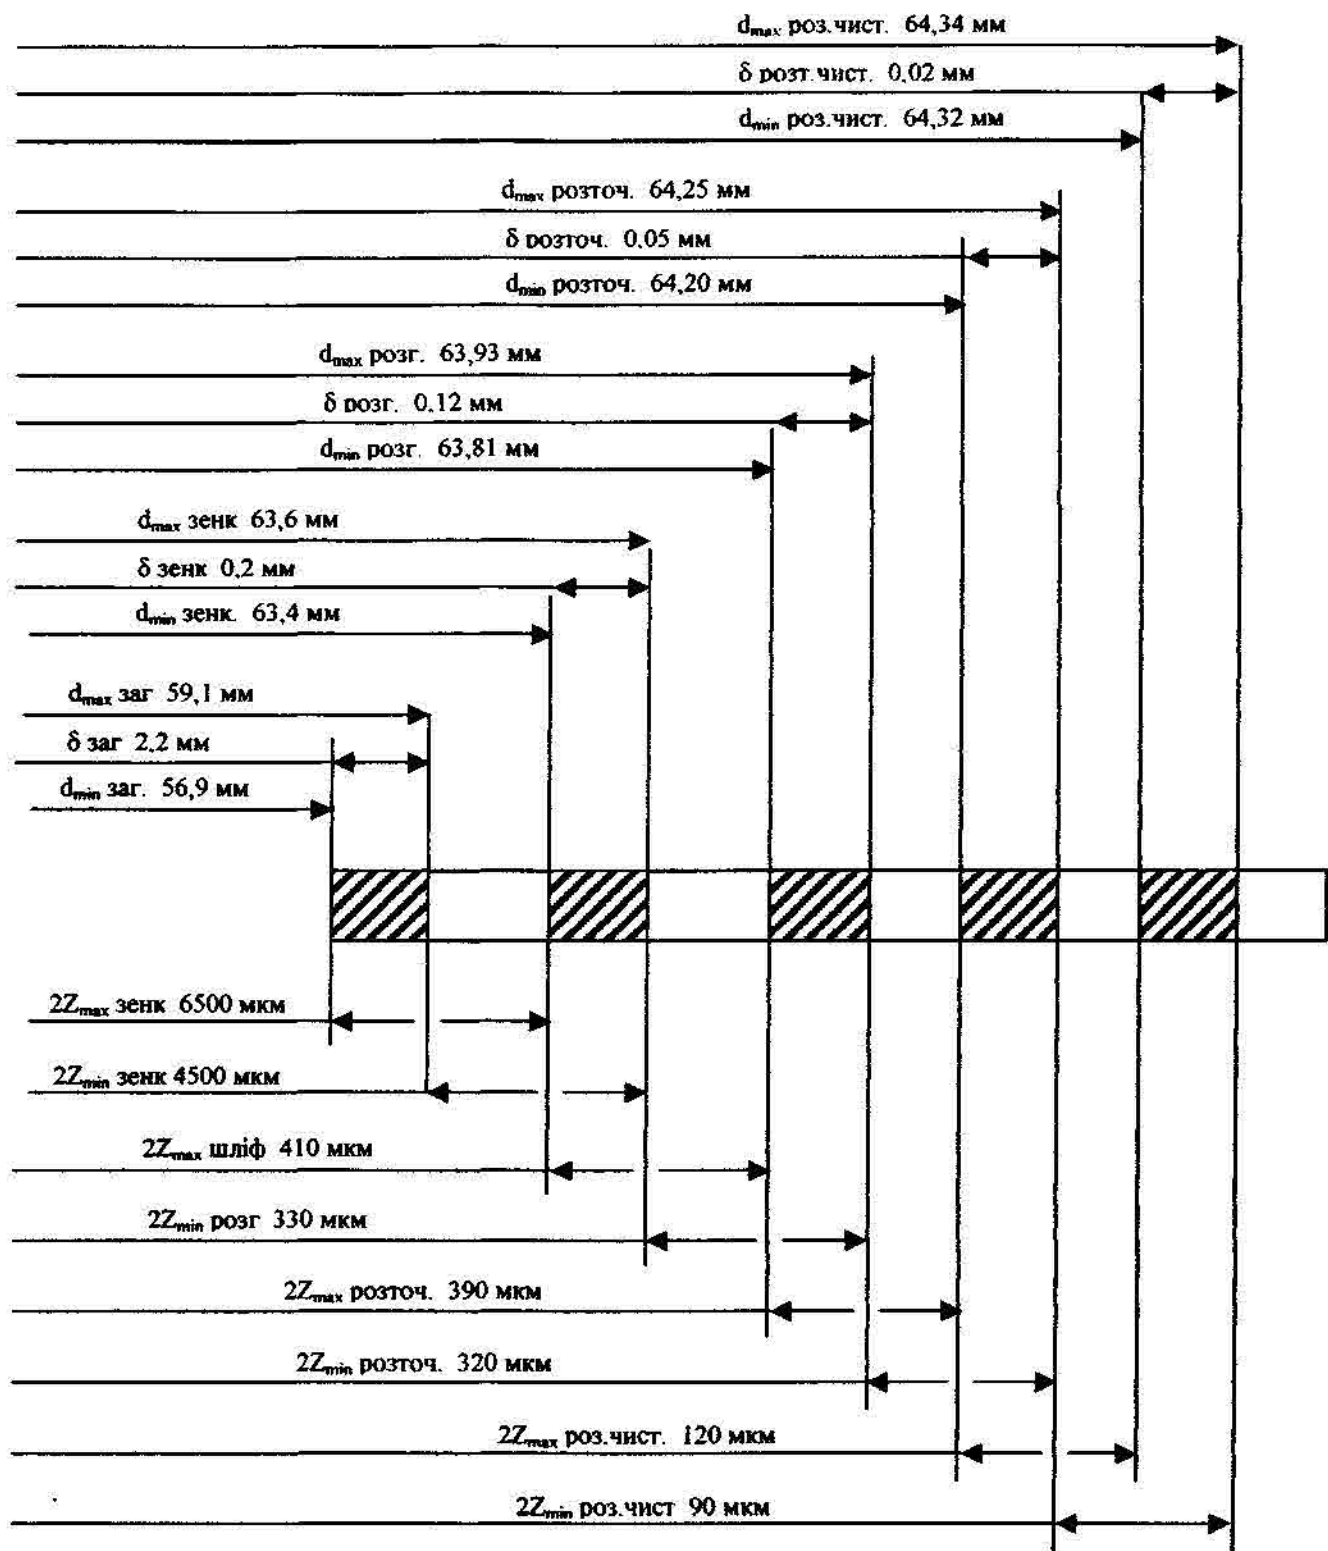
Схема графічного розташування припусків і допусків для обробки отвору
